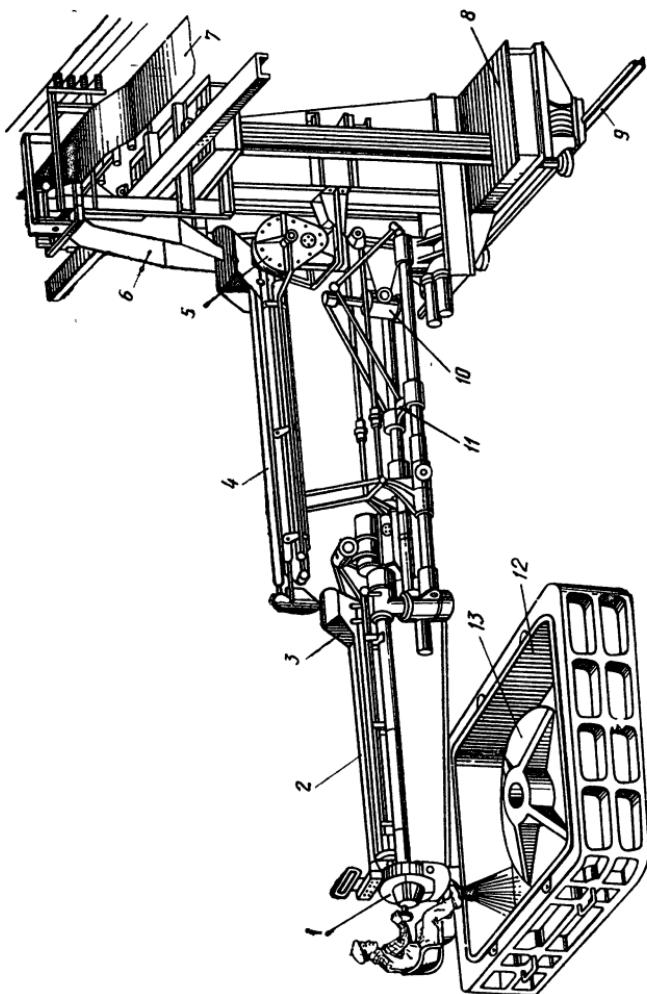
Формовка с помощью передвижного консольного пескомета:
